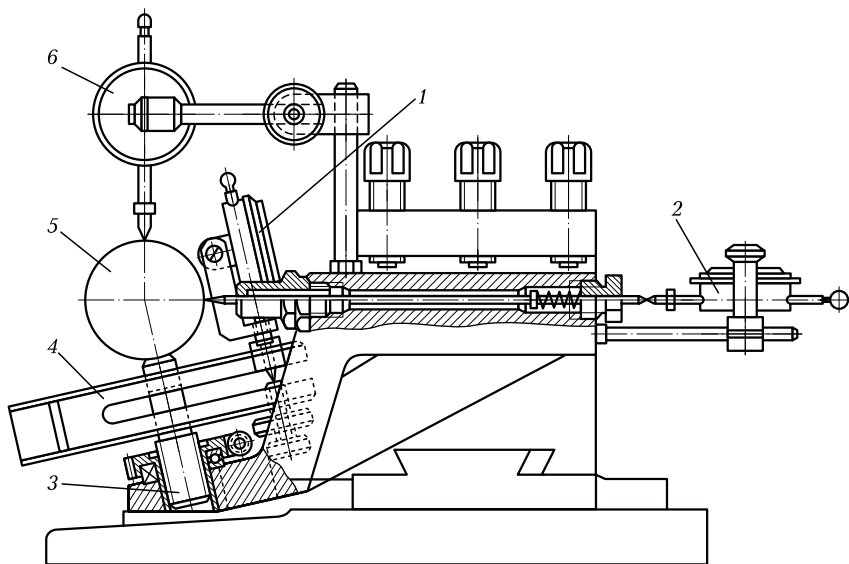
Схема проверки токарного станка на жесткость:
